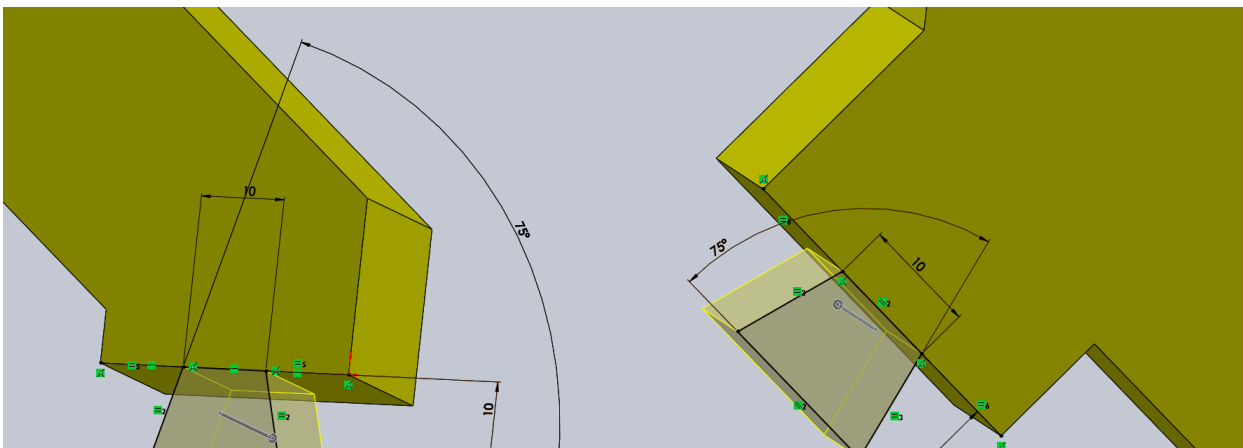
A la izquierda: cola de milano en de la posición vertical. A la derecha: cola de milano de la posición inclinado. Ambas se han realizado por una extrusión de 15mm.
